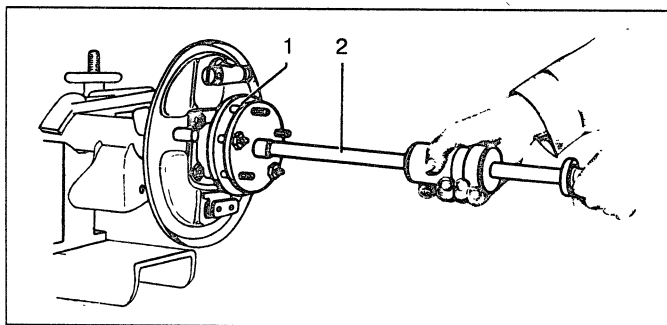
Выпрессовка полуоси: 1 – полуось; 2 – выталкиватель 67.7823.9516
